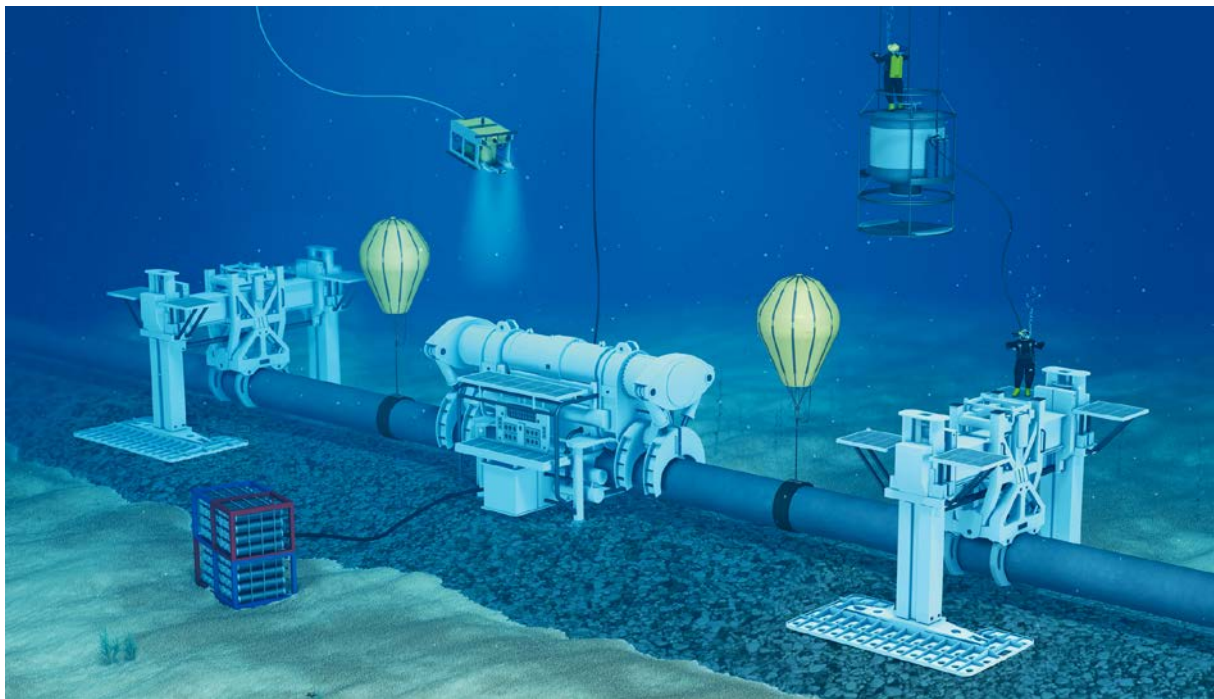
Einrichtung für Überdruckschweißen unter Wasser
